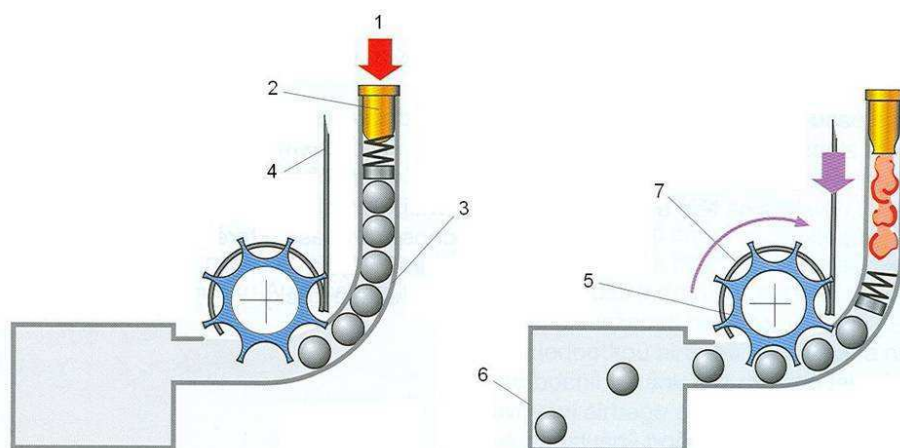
Pyrotechnické předpínání pásu [3]
